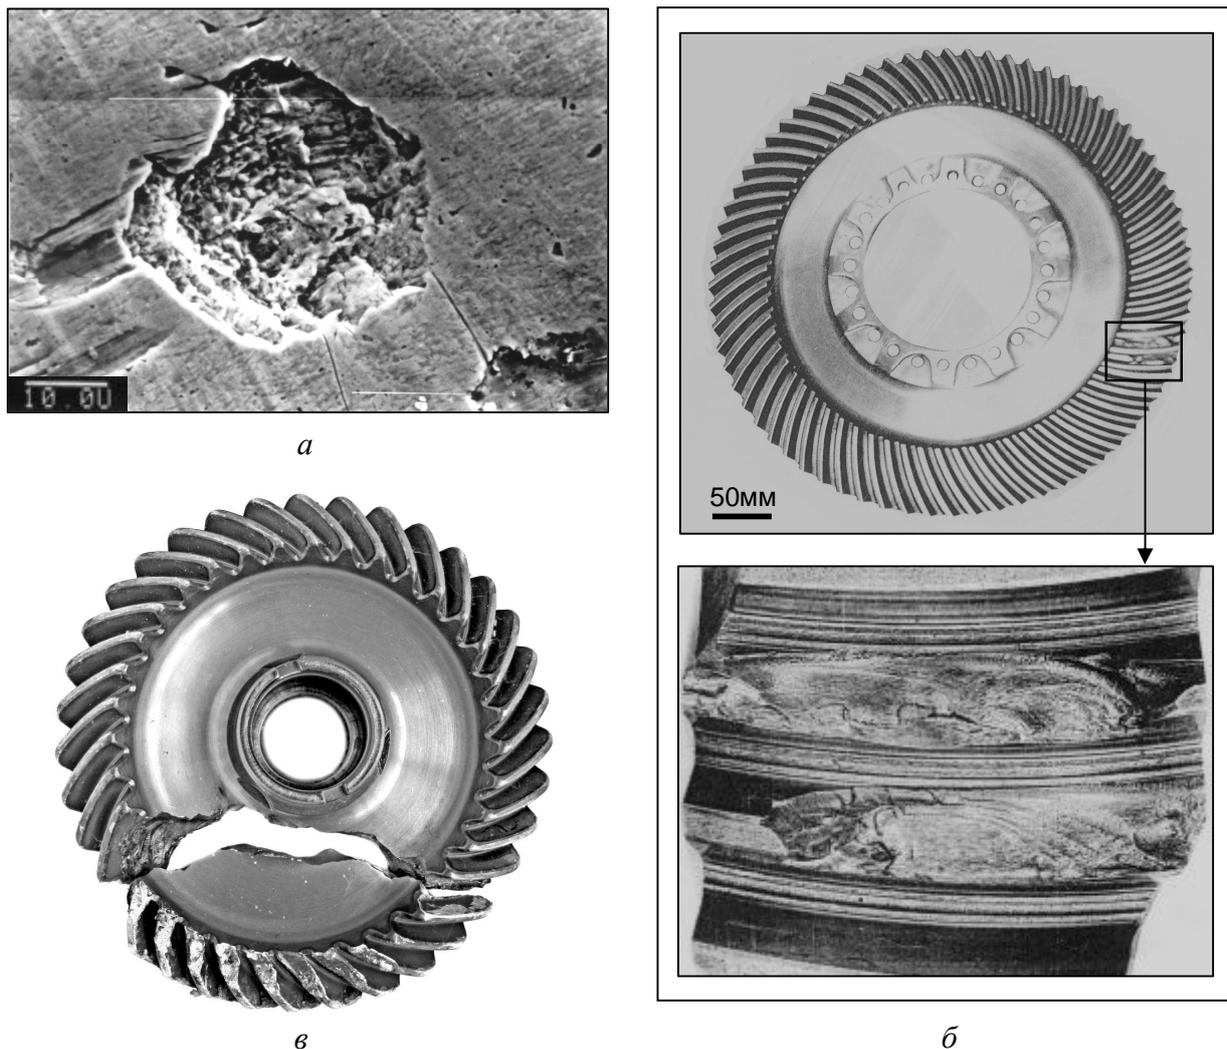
Типы усталостного разрушения конических зубчатых колёс: а – выкрашивание рабочей поверхности зуба, б – обрыв зуба, в – обрыв фрагмента зубчатого колеса
